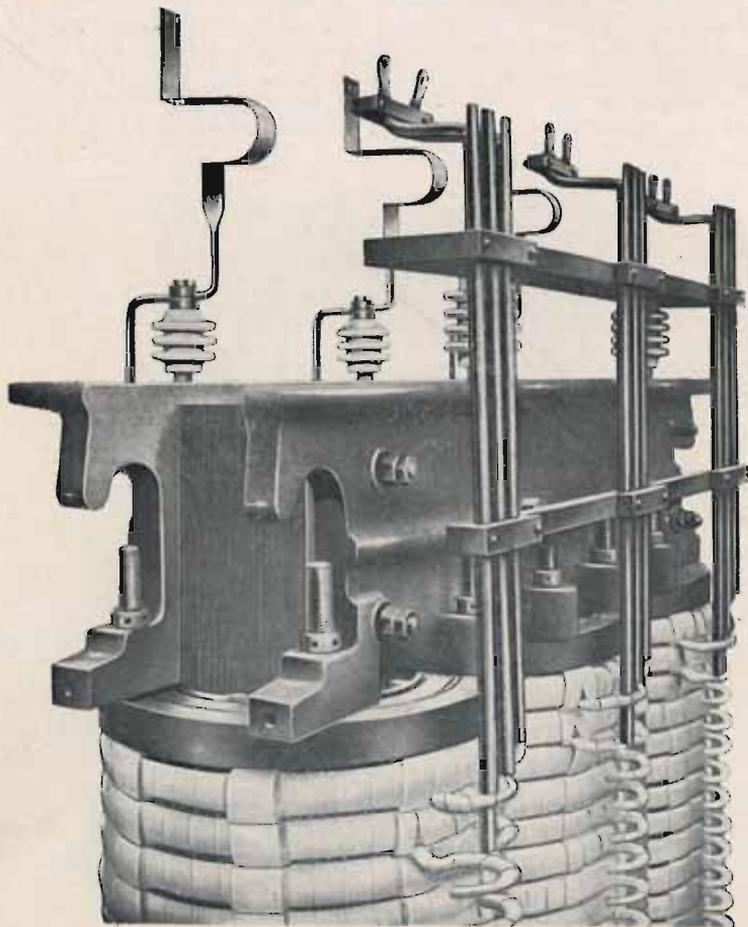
Calage des bobinages au moyen de vis de serrage.
